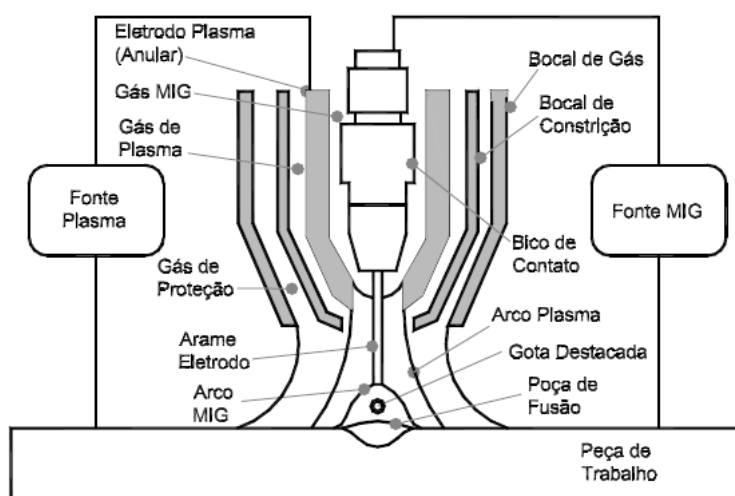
Desenho esquemático da pistola de soldagem Plasma-MIG com eletrodo anular de cobre (ESSERS, 1981, apud OLIVEIRA, 2006)
